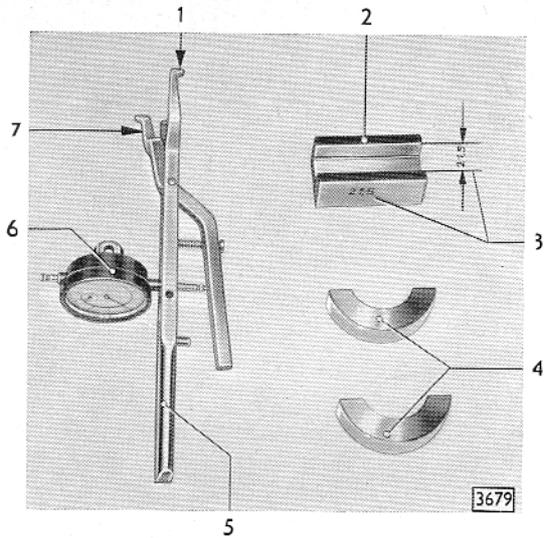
Zahnflankenspiel-Einstellwerkzeug S-1273
